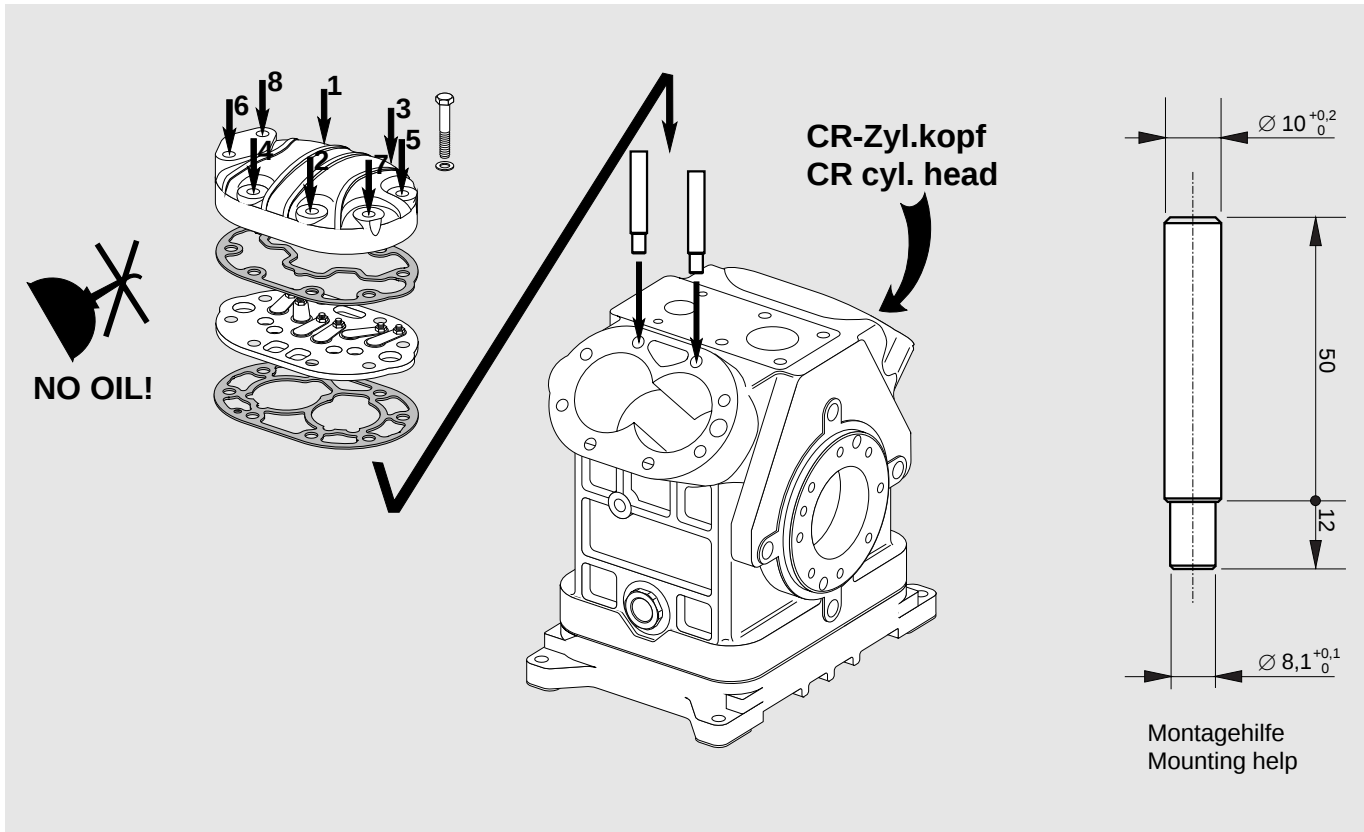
Austausch Ventilplatte / Zylinderkopfdichtung
